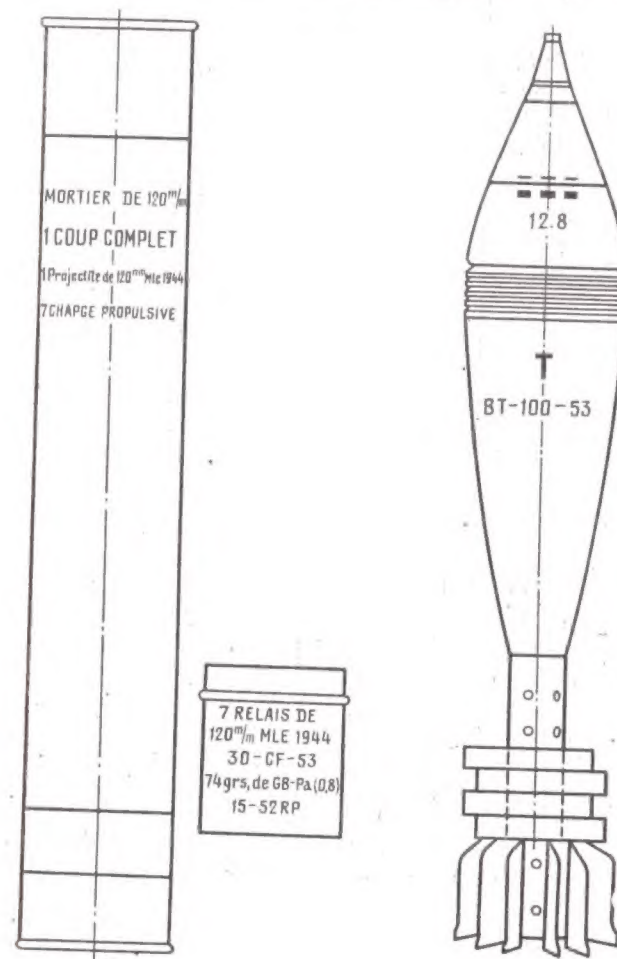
Образец маркировки мины М44, пенала для выстрела и упаковки для зарядов
